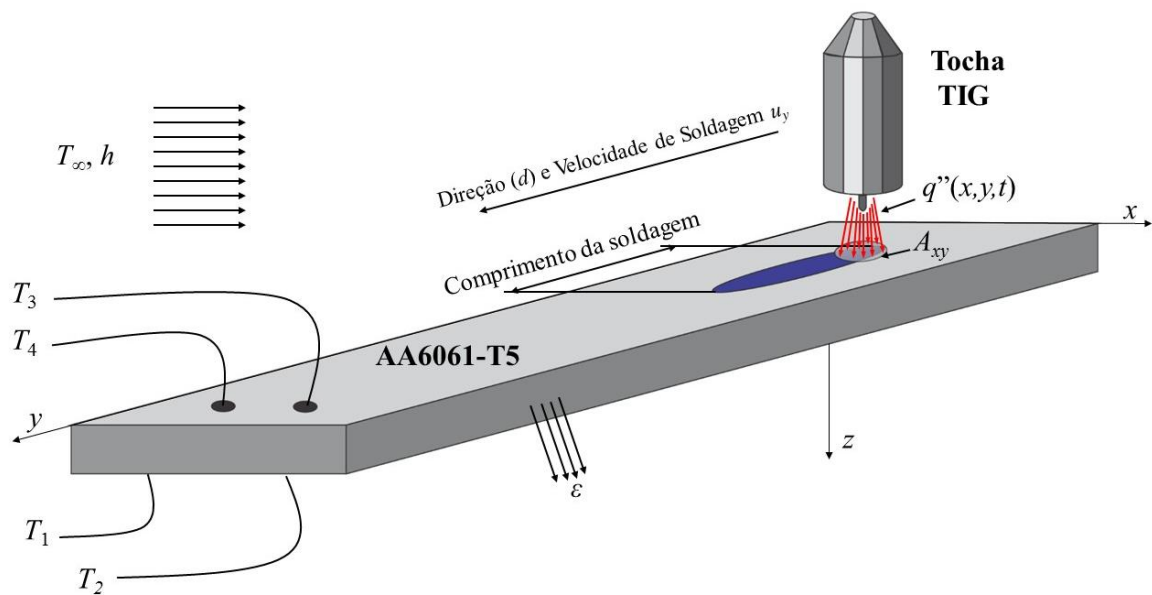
Representação tridimensional de um processo de soldagem TIG em alumínio.
